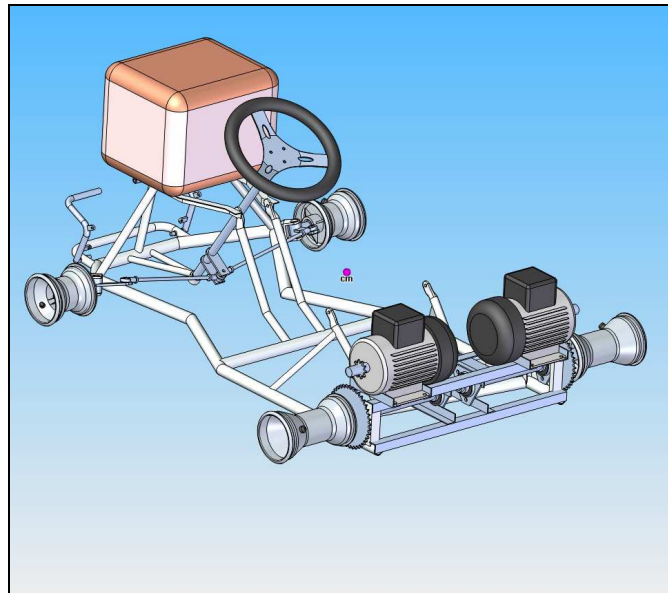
Imagen 3D del conjunto chasis – motores - generador
